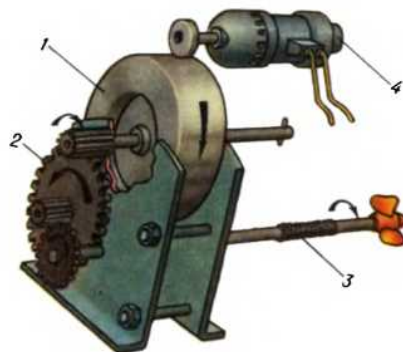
Устройство инерционного двигателя: 1 — маховик; 2 — редуктор; 3 — гибкий вал; 4 — пусковой отъемный электродвигатель с резиновым кругом.
